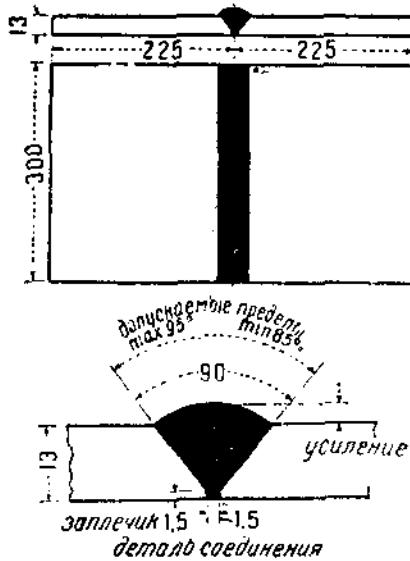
Сварка встык односторонним V-образным швом.
